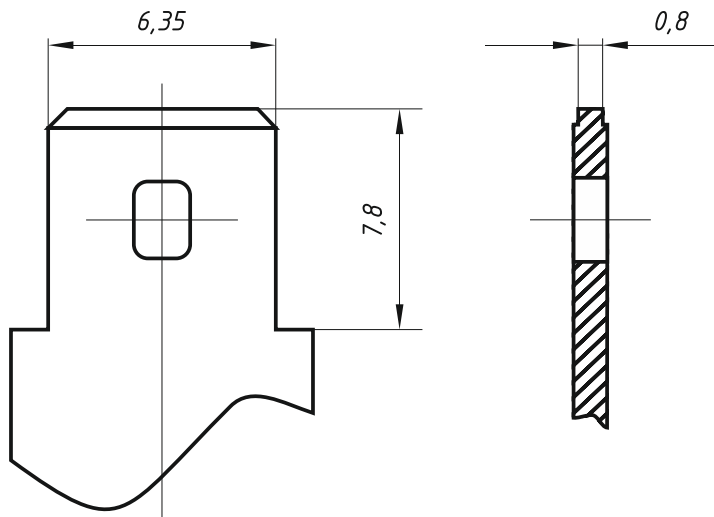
Внешний вид и габаритные размеры выводов подключения АБ
